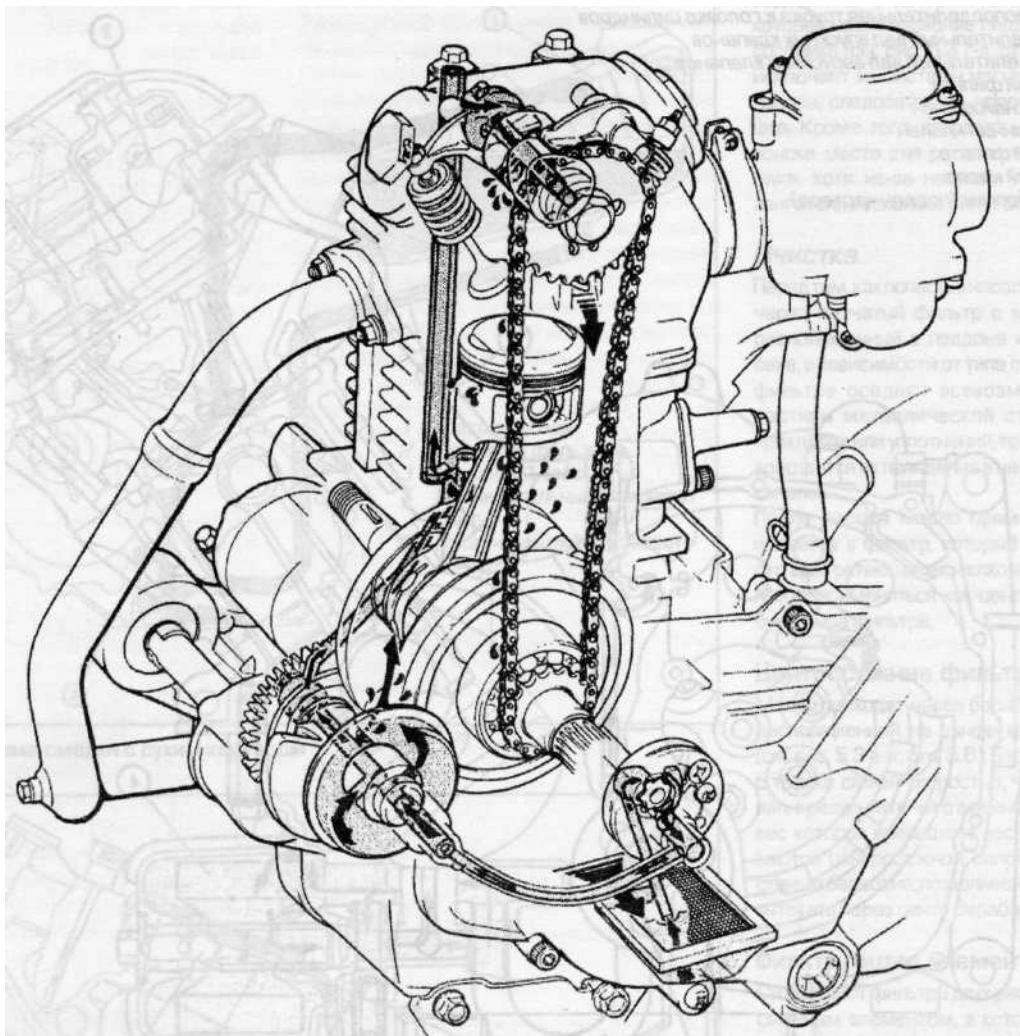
д Система смазки с мокрым картером одноцилиндрового двигателя
